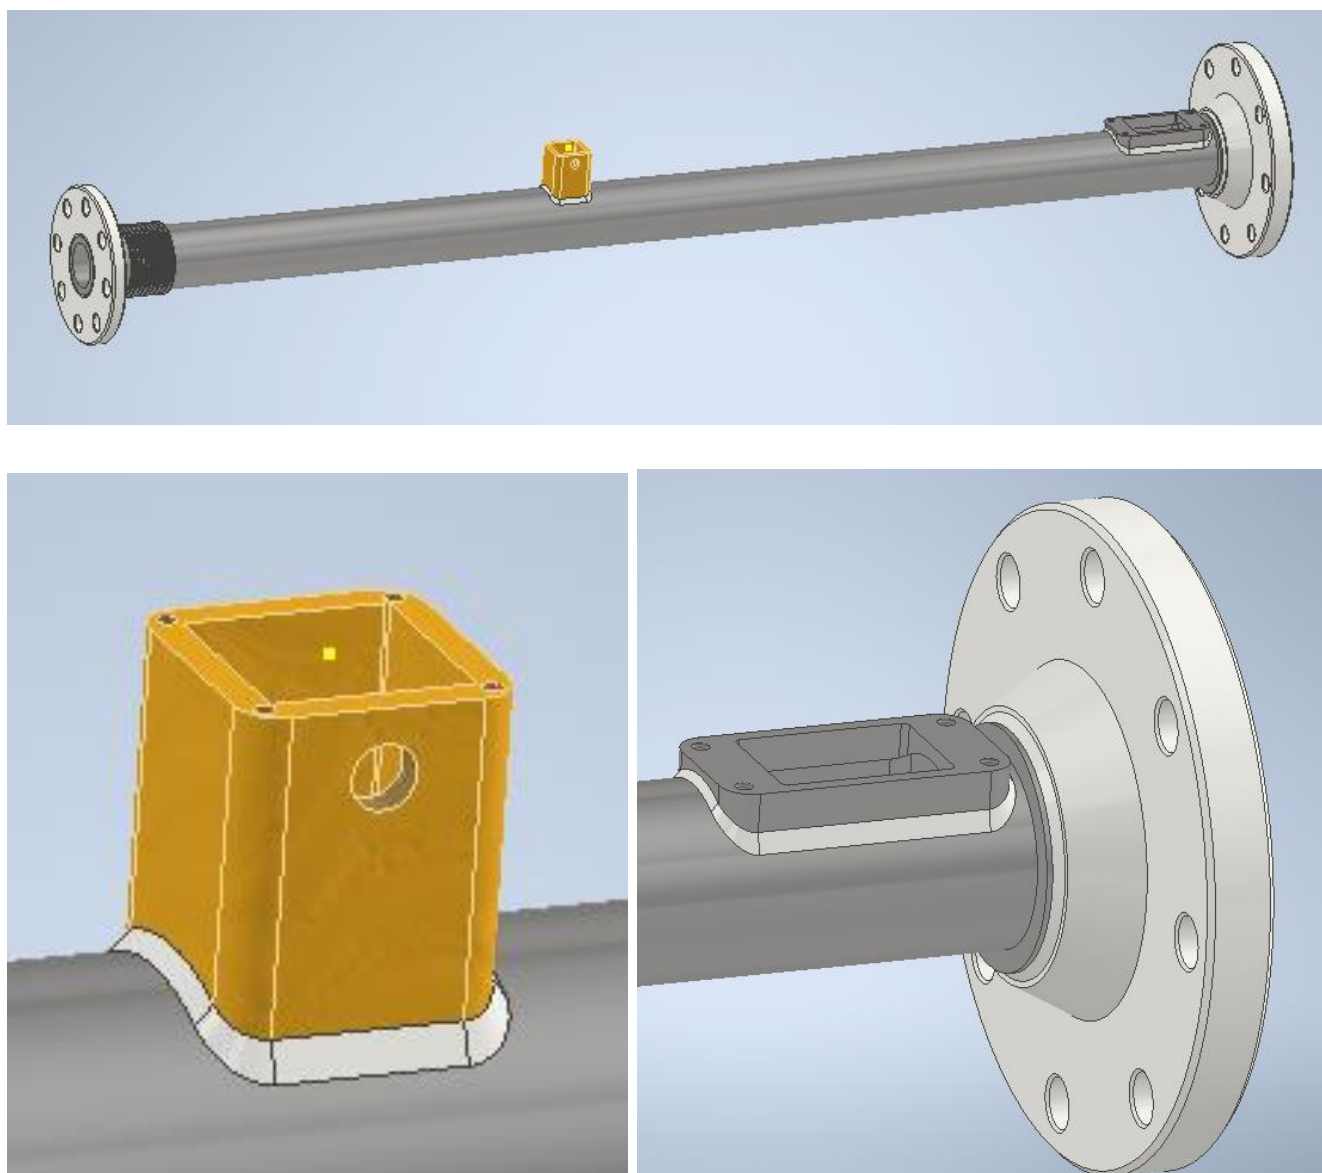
Вигляд збірки зварного корпусу екструдера.
